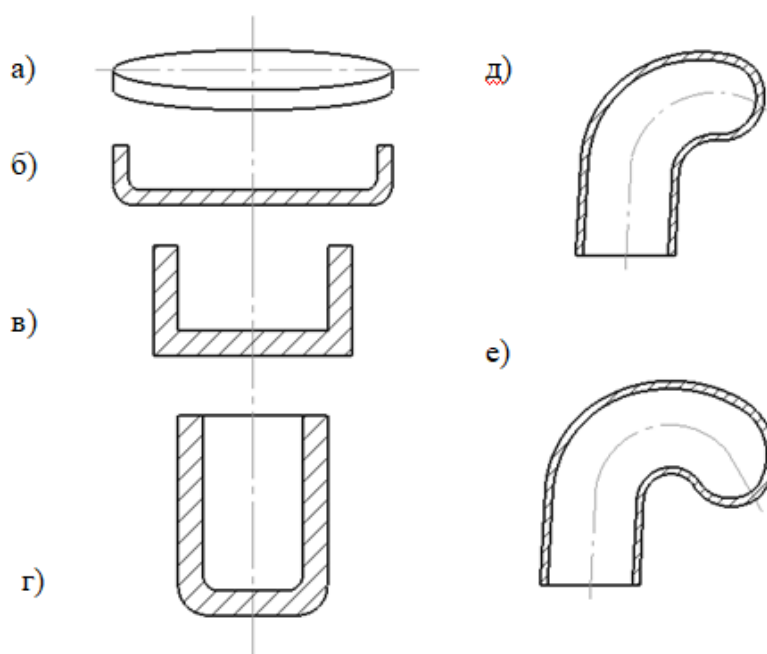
Формообразование газовода: а) заготовка; б), в), г), д) 1-4 этапы вытяжки; е) полученная заготовка
